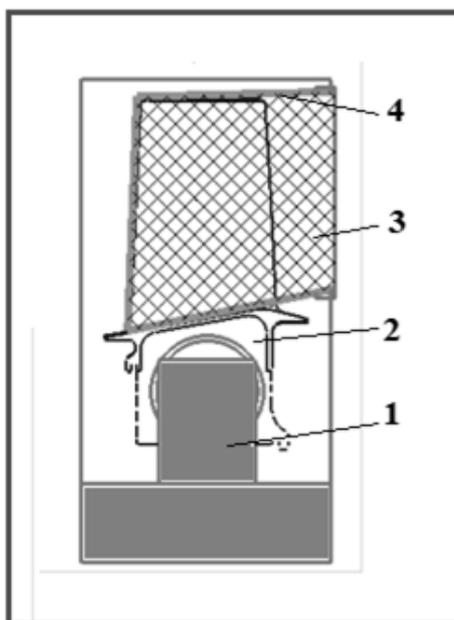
Схема обработки лопатки при использовании направляющих перемещения (1- держатель, 2 – лопатка, 3 – лента, 4 – направляющие)
